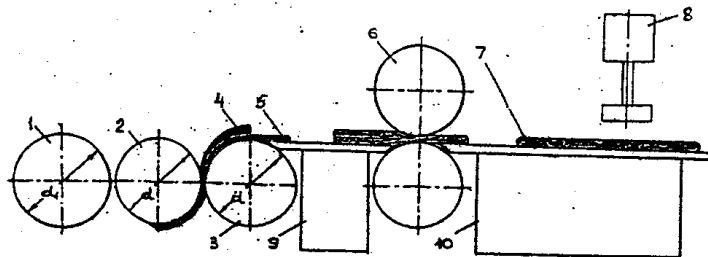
Новая ПМЛ для получения заготовок отрезных кругов: 1 и 2 — валки для смешения смесей; 2 и 3 — валки для прокатки листовых полуфабрикатов; 4 — нож; 6 и 7 — промежуточная и чистовая клетки дуо; 8 — вырубной пресс; 9, 10 и 11 — промежуточные и выходной столы
